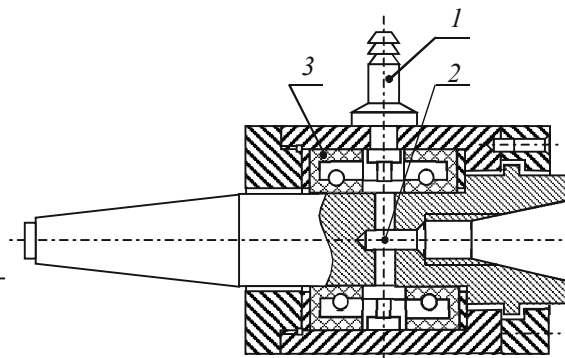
Оправка для крепления алмазного сверла в шпинделе станка: 1 – штуцер; 2 – полость; 3 – манжета
